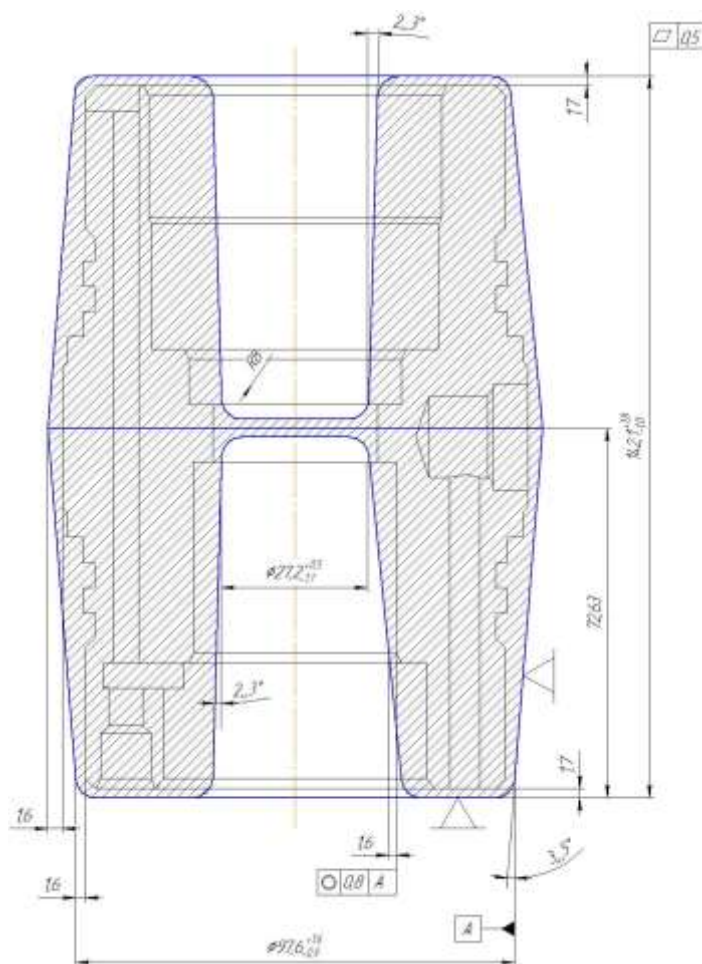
Эскиз поковки с предварительными размерами
